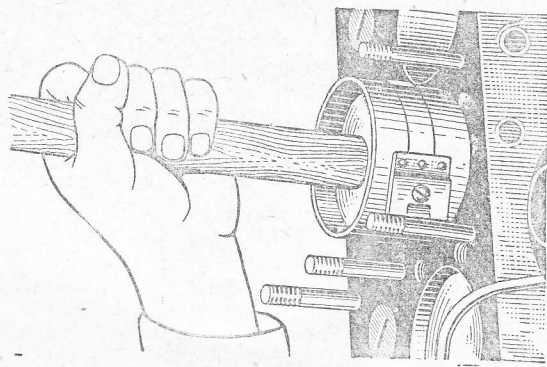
Установка в цилиндр поршня в сборе с поршневыми кольцами.
